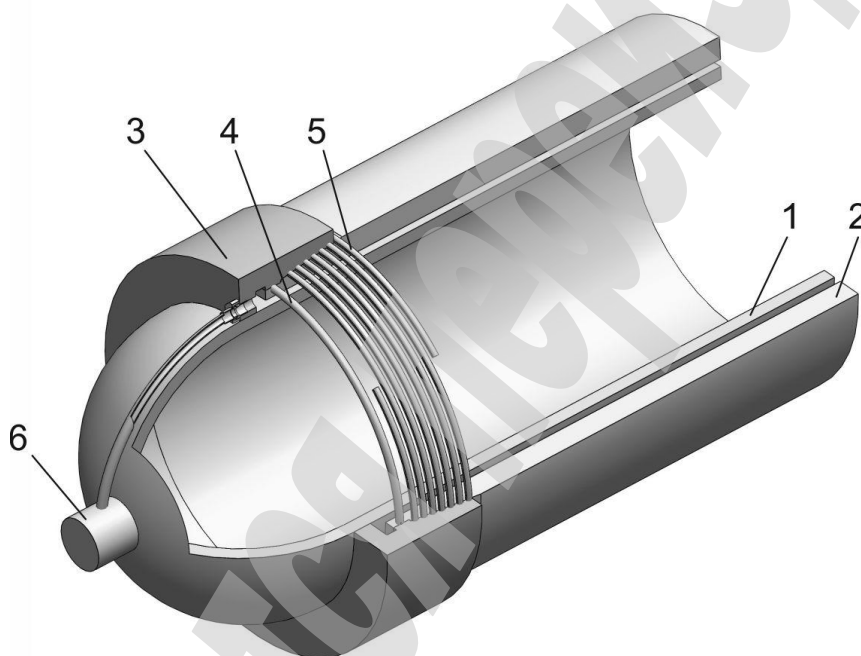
Схема конструкції багатопорожнинної посудини високого тиску, утвореної з використанням композитної і сталеві труби: 1 – сталеві труба з напівсферичним днищем; 2 – композитна труба; 3 – сталеві напівмуфта; 4 – ущільнюючий елемент; 5 – вставний фіксуючий елемент; 6 – мультиклапан
